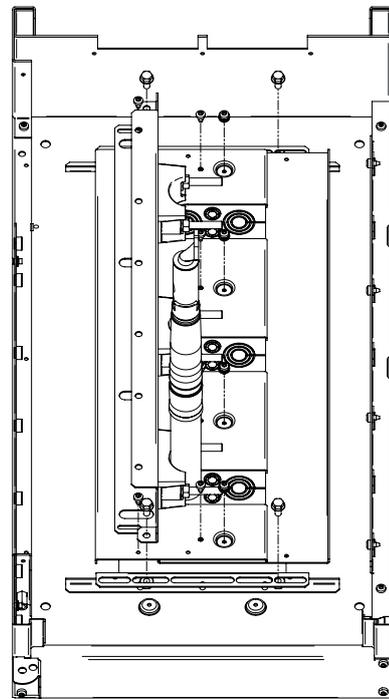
Installazione delle lamiere del pavimento, dei listelli guidacavi, dei serracavi e dei passacavi
